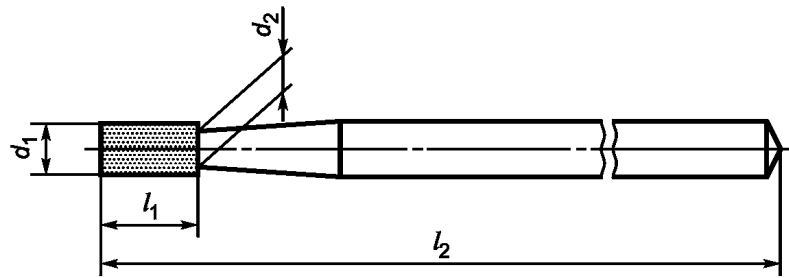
Цилиндрическая рабочая часть с длиной головки 3,0 мм
